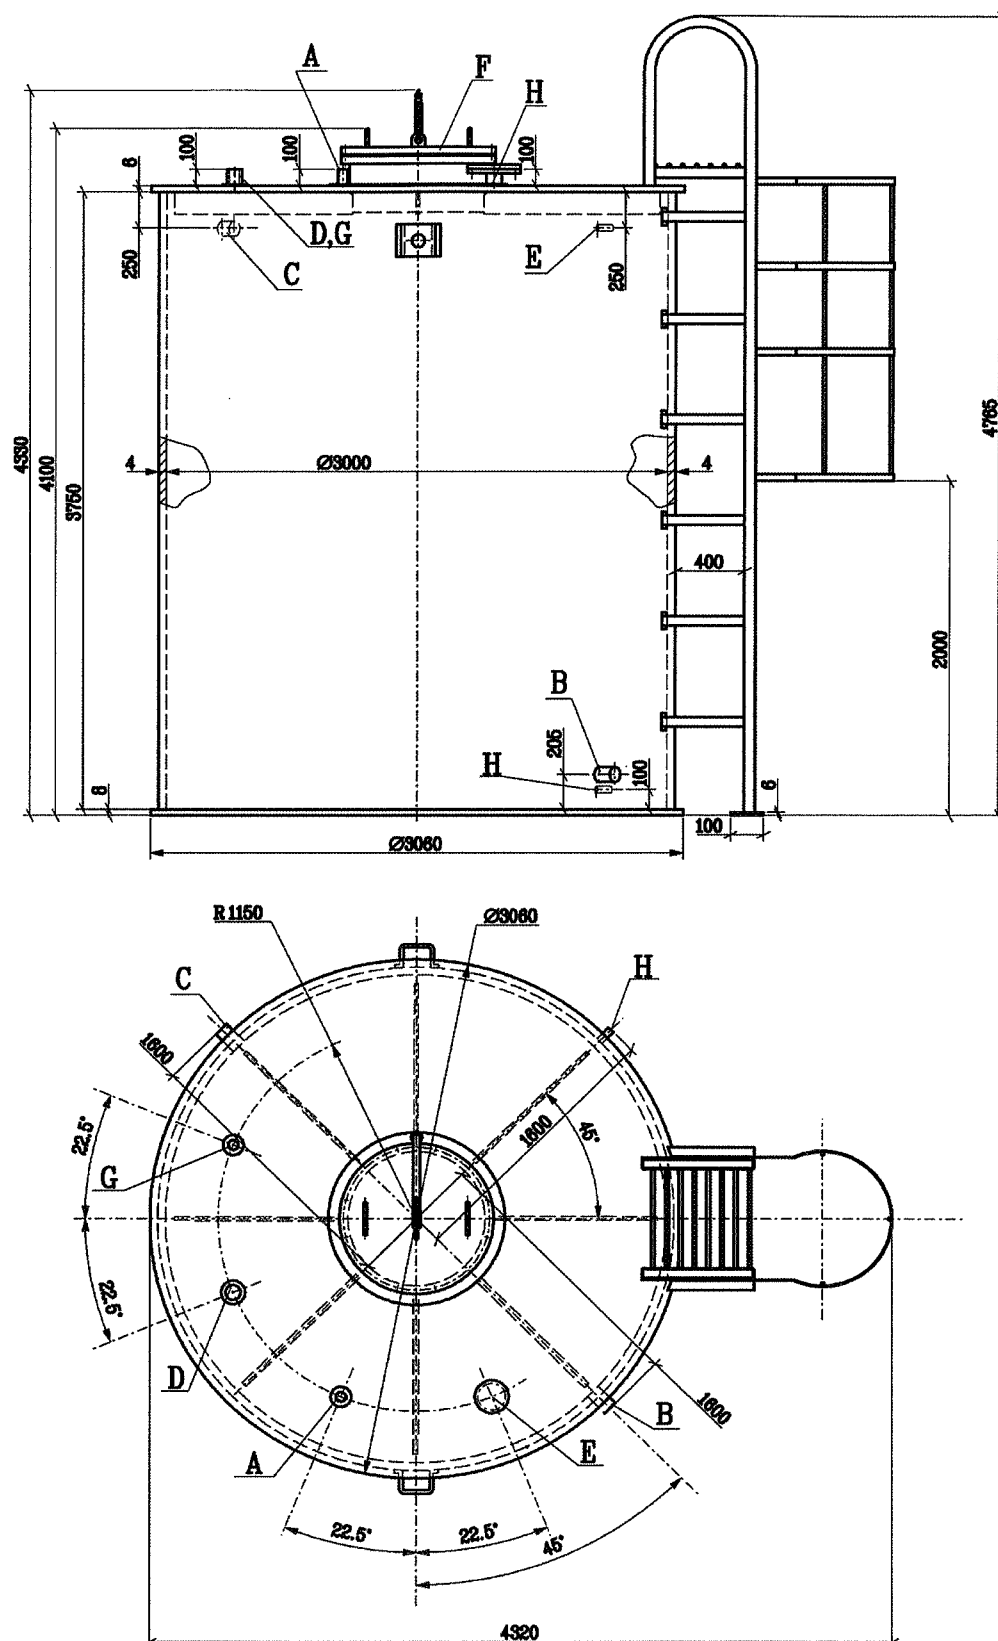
Габаритный чертеж бака приема и хранения аммиака QCF10BB001, QCF10BB002
